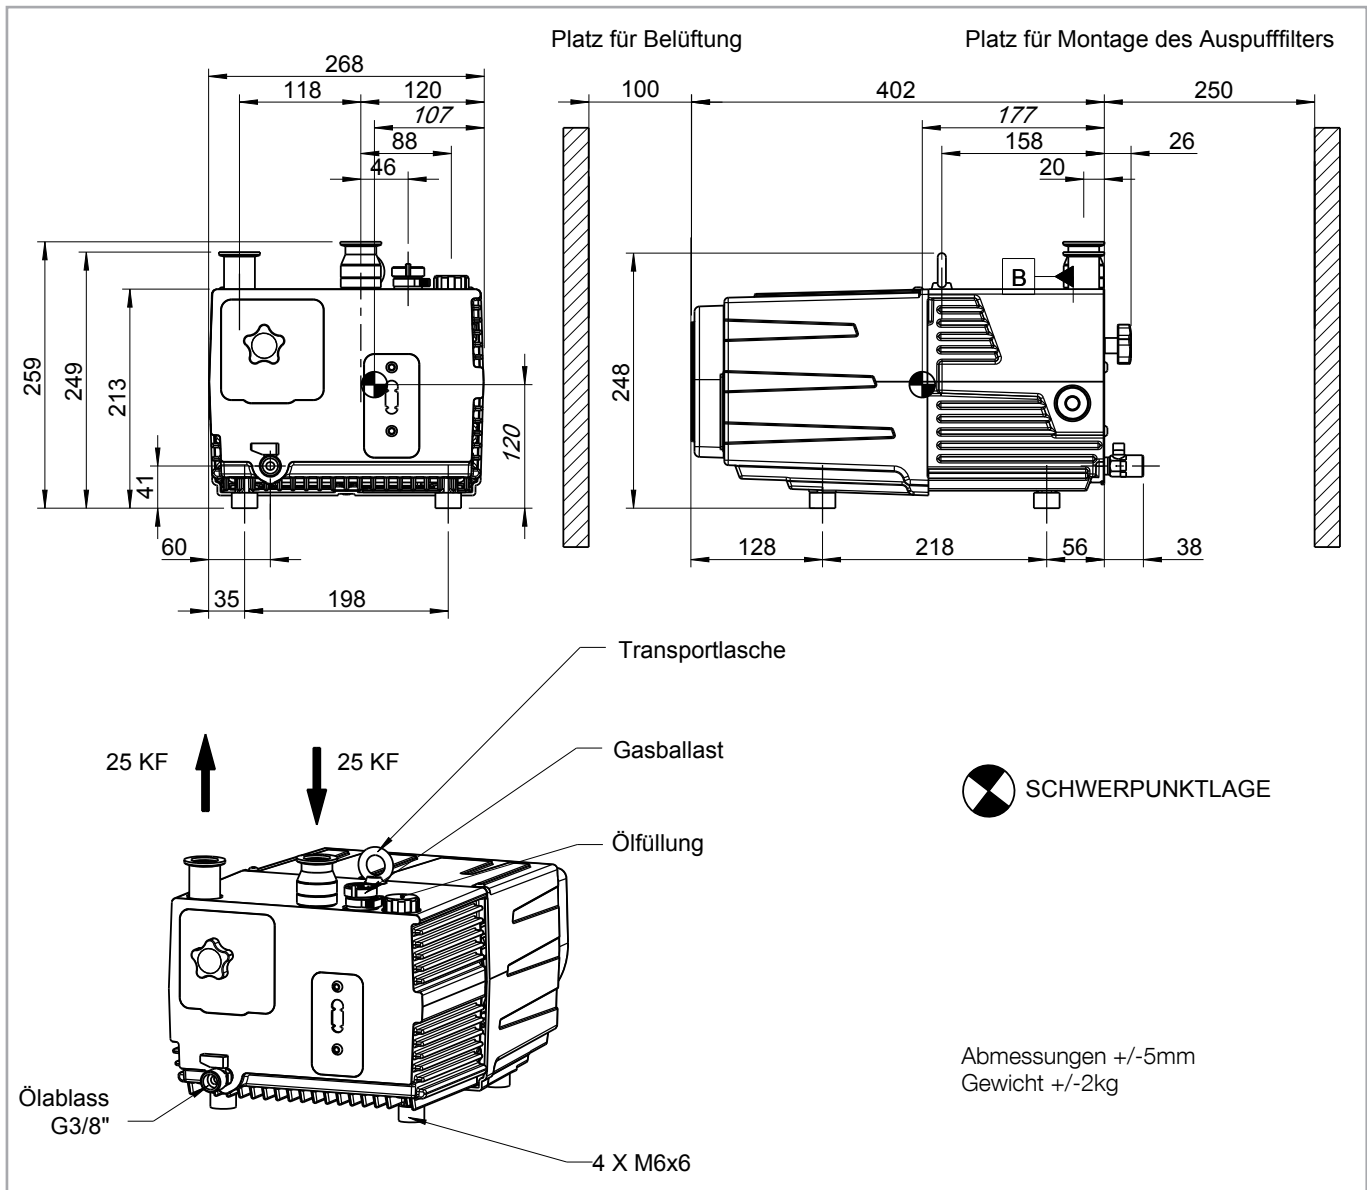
Maßzeichnung der SV16 DI und SV25 DI
